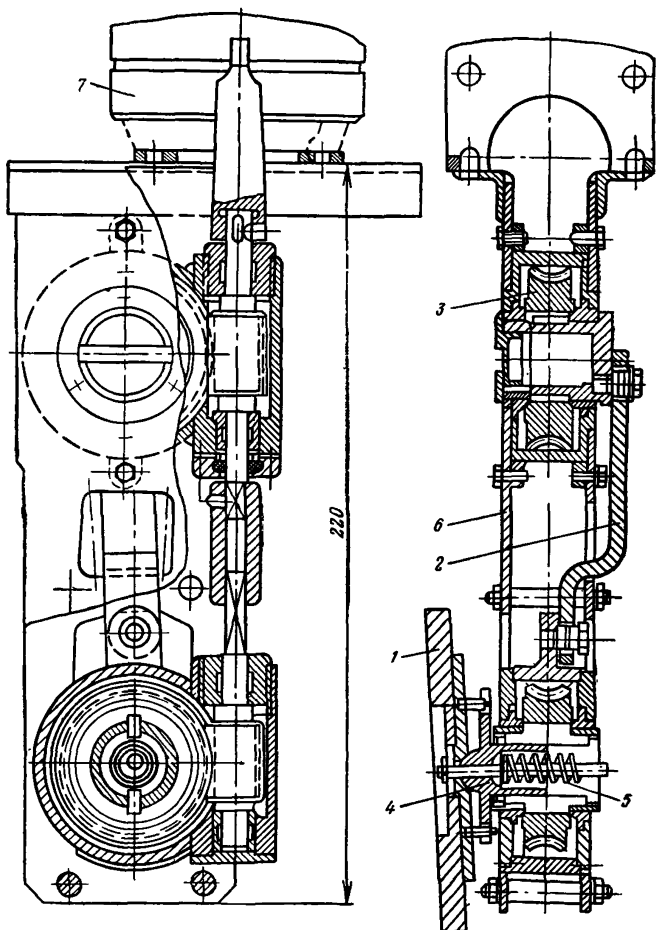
Приспособление для притирки седел задвижек Ду 100—250 мм:
